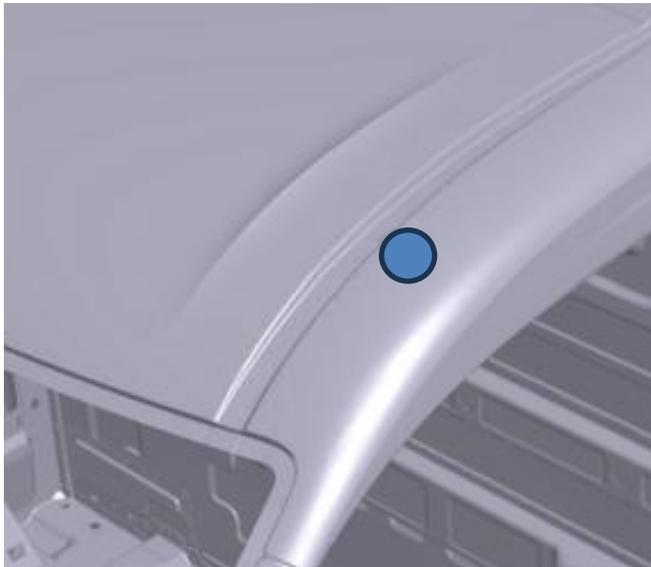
Préparation du passage de câble pour les feux de position – Ouverture dans la zone du pavillon (ici côté gauche représenté)
